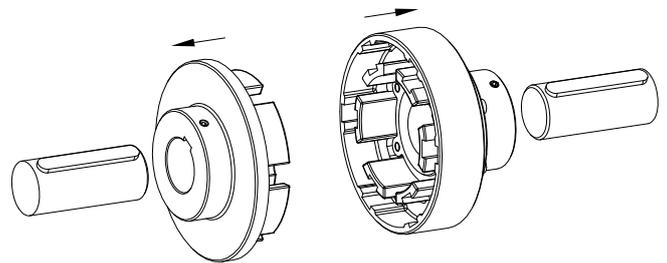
Montaggio dell'elemento a settori frontali e della flangia del mozzo con l'anello a settori frontali
